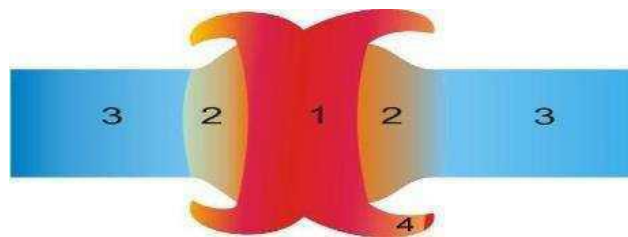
Prinsip kerja pengelasan gesek (*friction welding*) (Khan, 2007)
